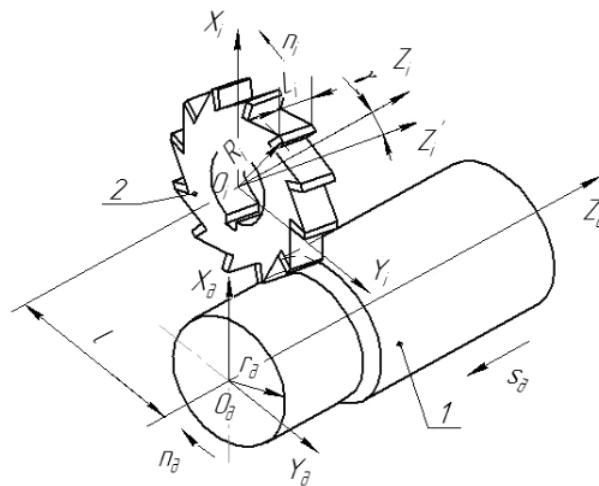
Схема фрезерування циліндричного вала зі схрещеними осями інструмента та деталі
